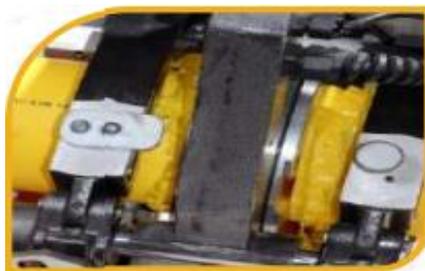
Procedimiento para la soldadura de termofusión a tope
